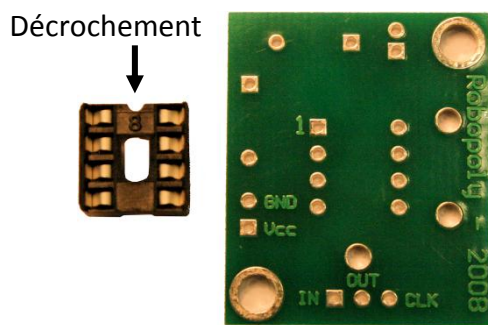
Socle dans la bonne direction et sur le bon côté du PCB
